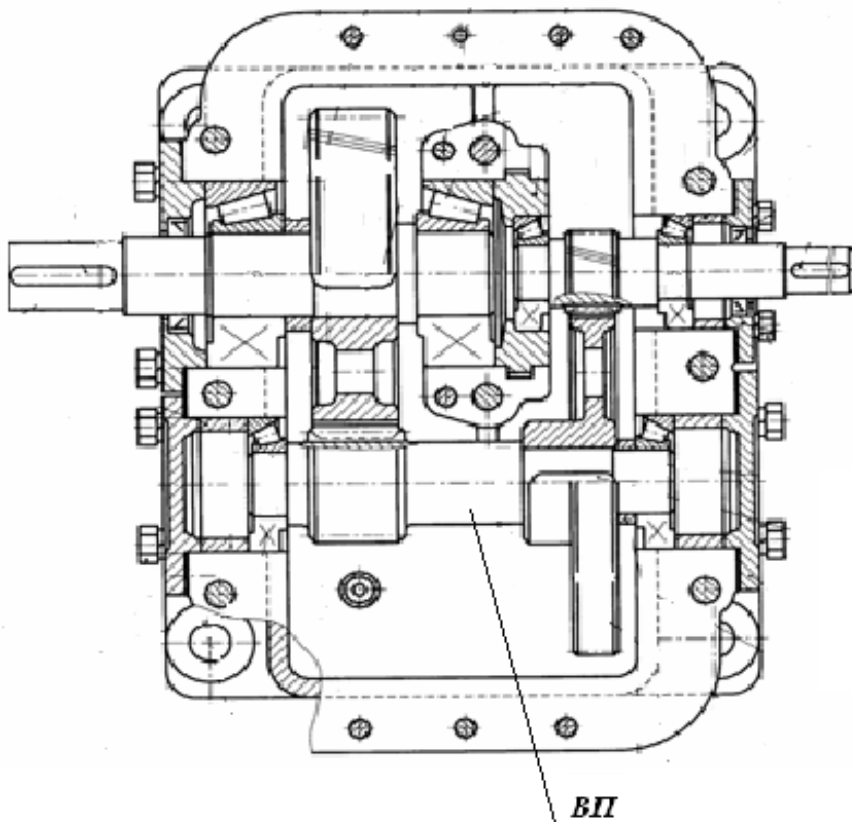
Цилиндрический двухступенчатый соосный редуктор
